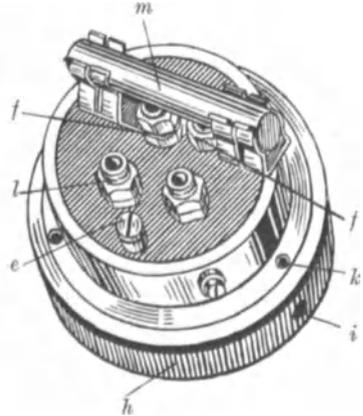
Universal-Röhrensockel der Irotechnik, Rückseite.
